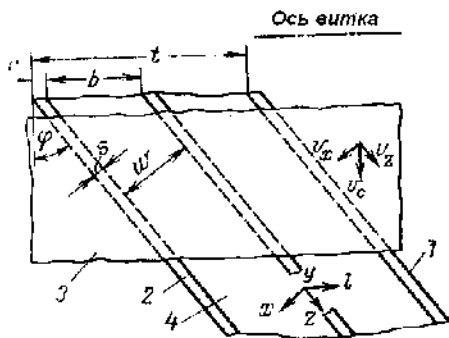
Развёртка винтового канала шнекового пресса на плоскости: 1 – стенка канала; 2 – развёртка витка; 3 – поверхность корпуса; 4 – канал.
